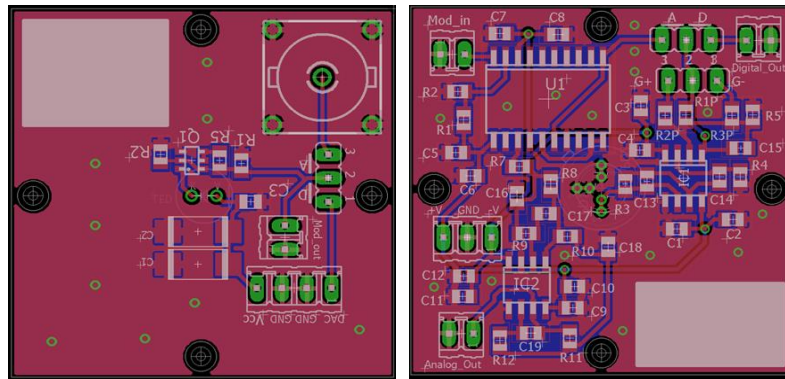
Diseño en Eagle de la placa PCB emisora (izq.) y detectora (drcha.).
